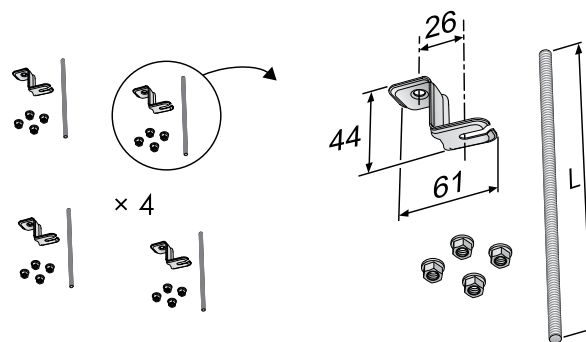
Монтажная деталь SYST MS M6-1: крепление и шпилька
